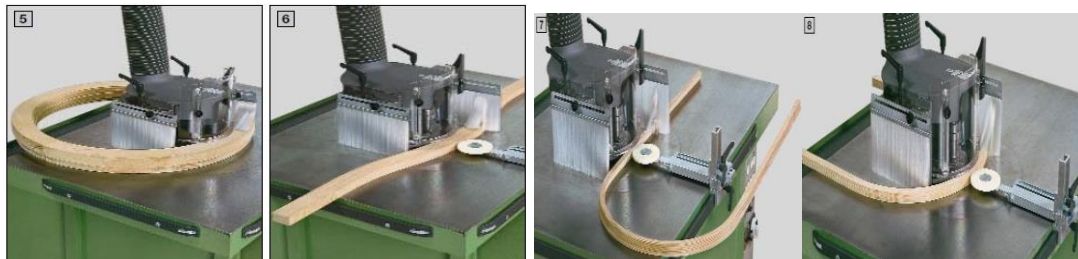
Freze makinesinde kavisli parça işlemede ek tabla, siper ve robot kullanımı[27].
